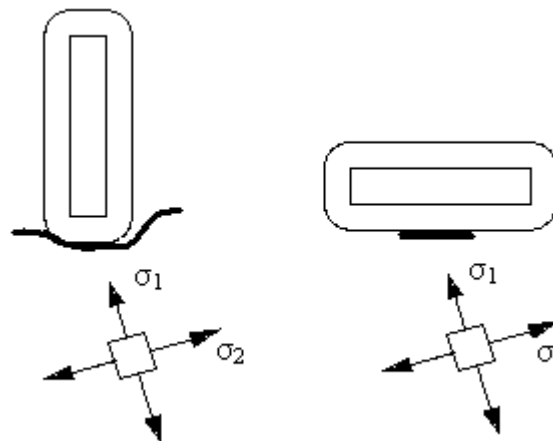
Crecimiento de grietas a lo largo del pie de la soldadura debido al esfuerzo principal σ_1 , predominantemente perpendicular al pie de la soldadura. Ref [14]
